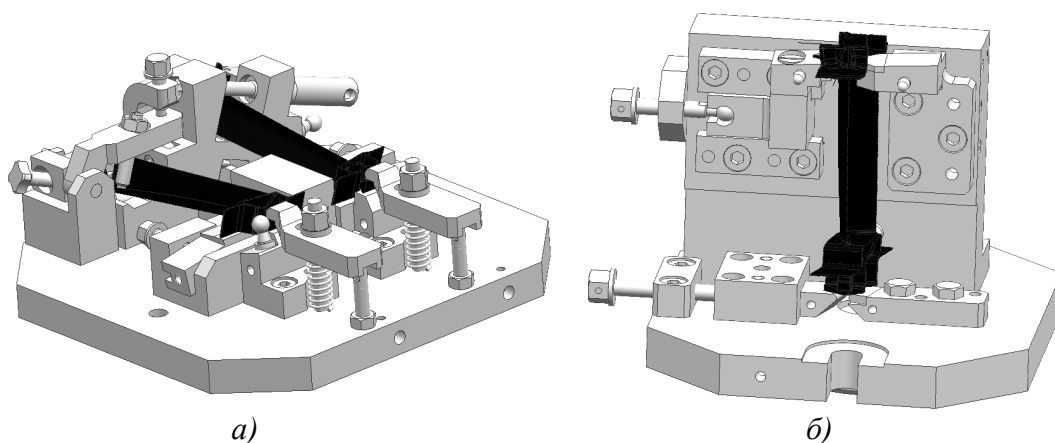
Специальные однопозиционные станочные приспособления для обработки лопатки турбины: а) плоскости замковой части лопатки, б) поверхностей бандажной полки
